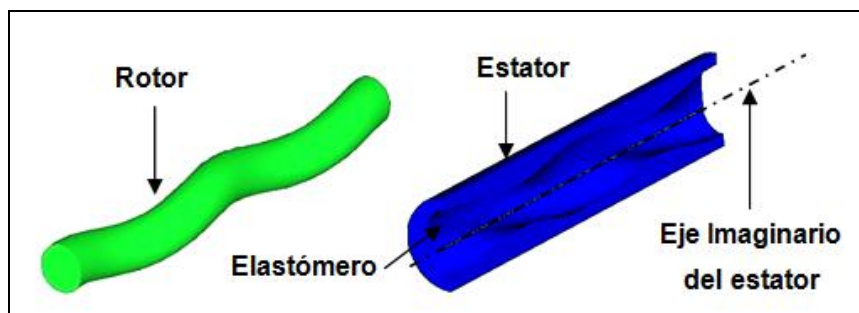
Principales componentes de una bomba de cavidades progresivas^[26]
